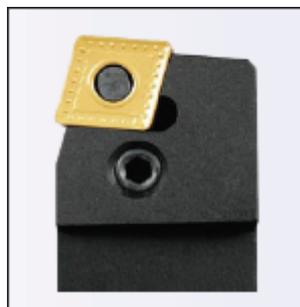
Конструктивные параметры токарного резца PCBNR4040S25
